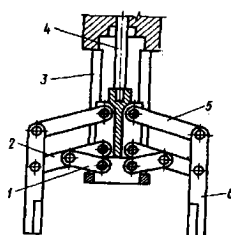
Центруючий широкодіапазонний захоплювач: 1, 2, 5 – важелі; 3 – корпус; 4 – тяга; 6 – губки
